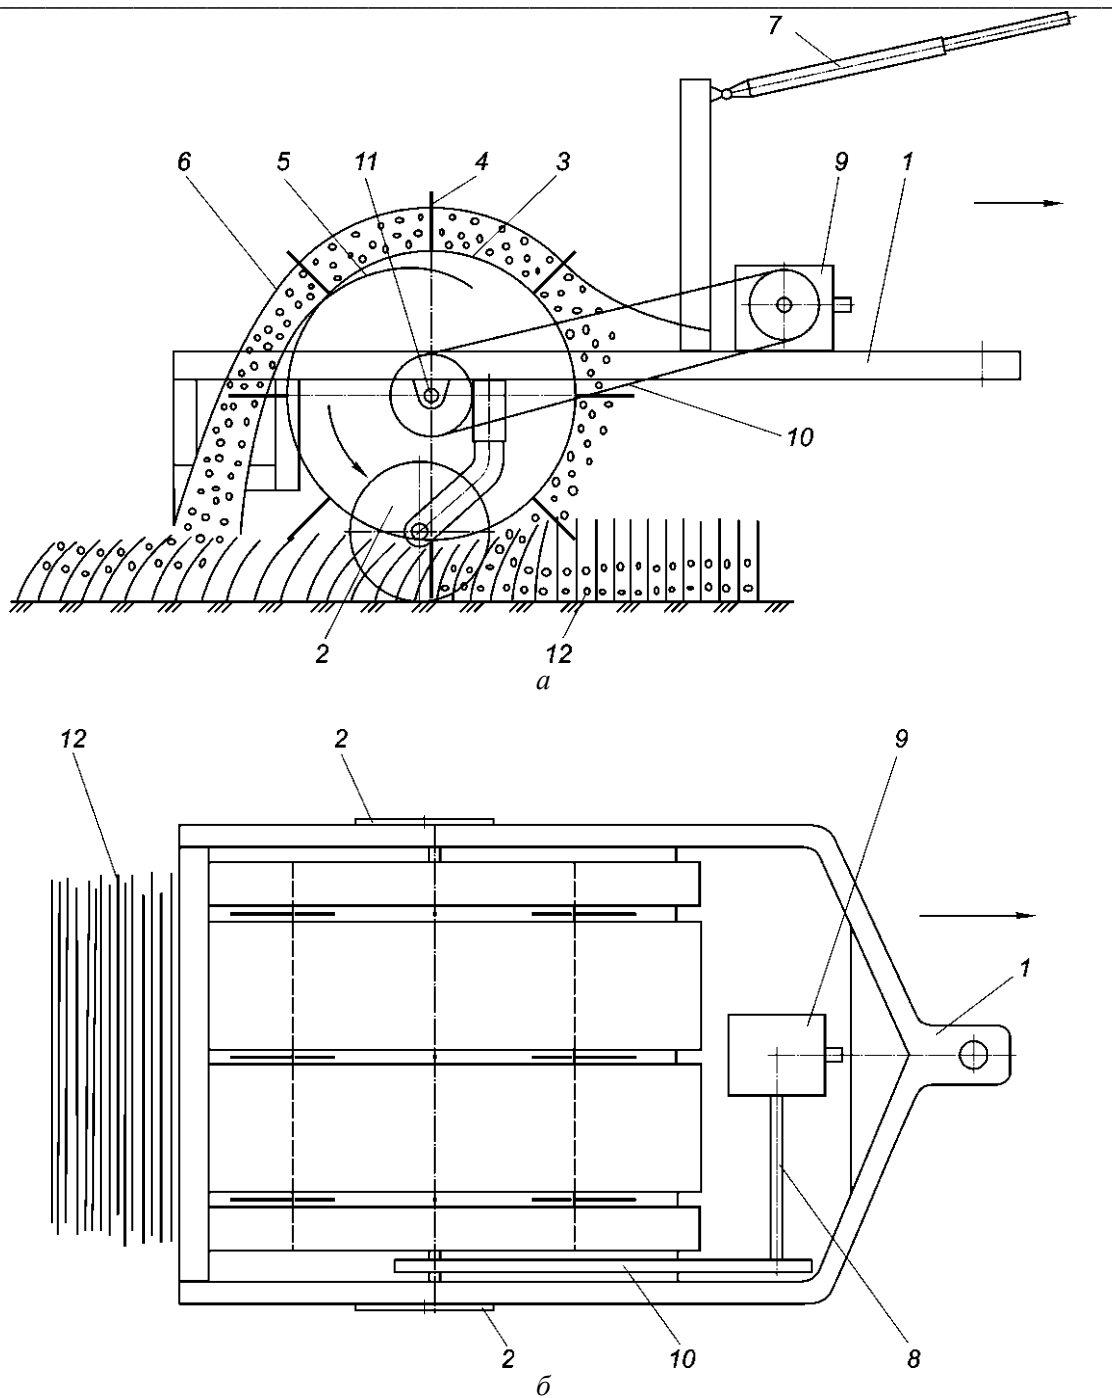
Схема ворушилки стрічок льону ВЛ-2: 1 – рама; 2, 4 – вали; 3 – колесо опорно-приводне; 5 – диск; 6 – зуб; 7 – решітка знімна; 8 – уповільнювальна ланцюгова передача
